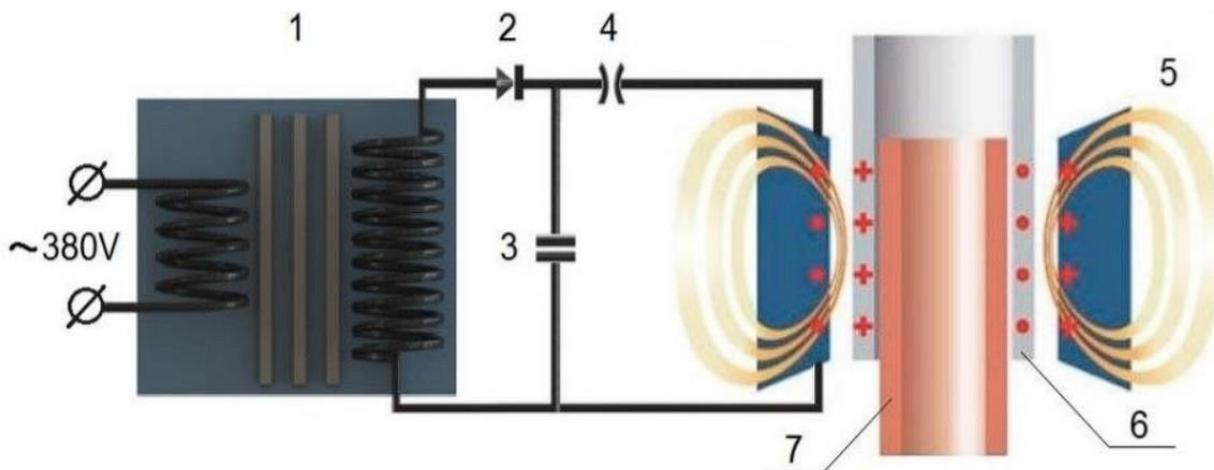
Принципиальная схема электрической цепи для магнитно-импульсной штамповки деталей:
